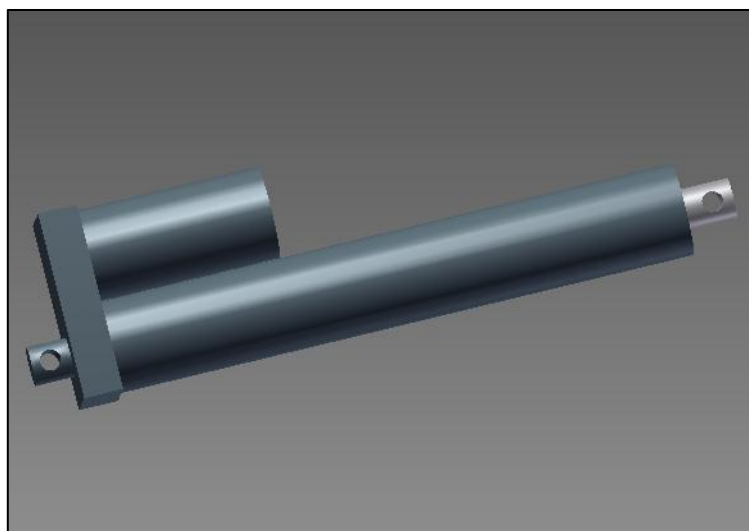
Dibujo CAD del actuador lineal Electra 1 S24-09A4-06.
